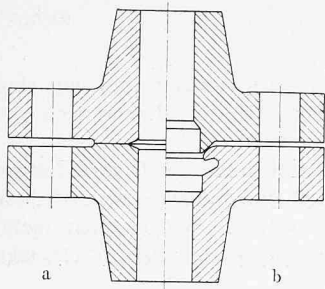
Flanschverbindung für hohe Temperaturen. a Ausführung nach DIN 2548, b Ausführung nach New Pipe Joints Challenge Welding Flanges. «Power» 115 (1971), Nr. 1, S. 76/77
